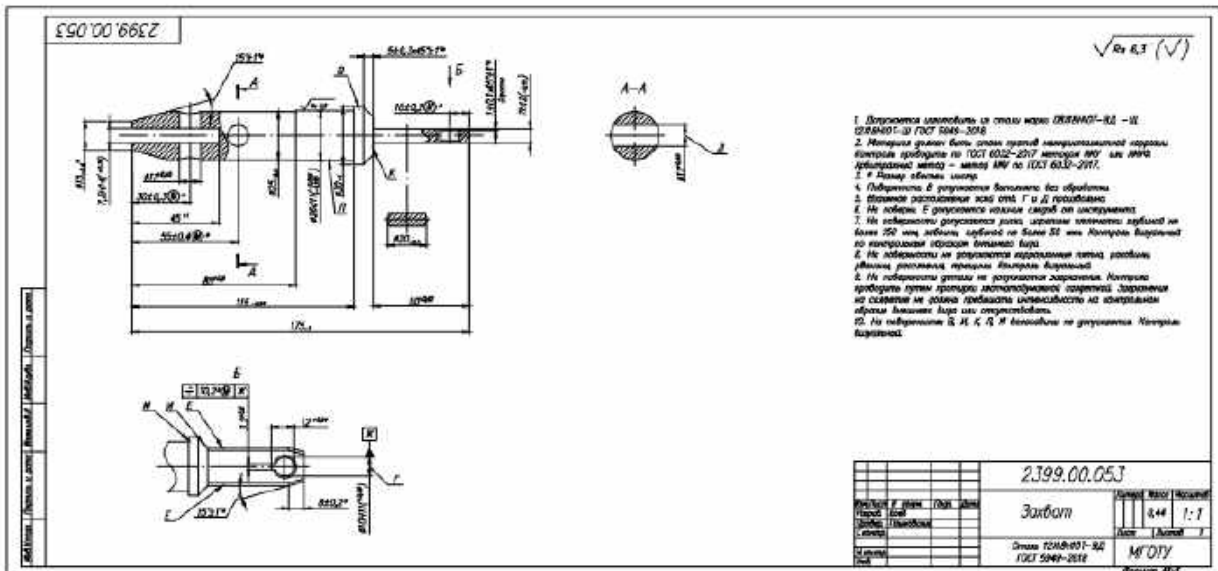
Захват транспортировочной заглушки (рабочий чертёж)
